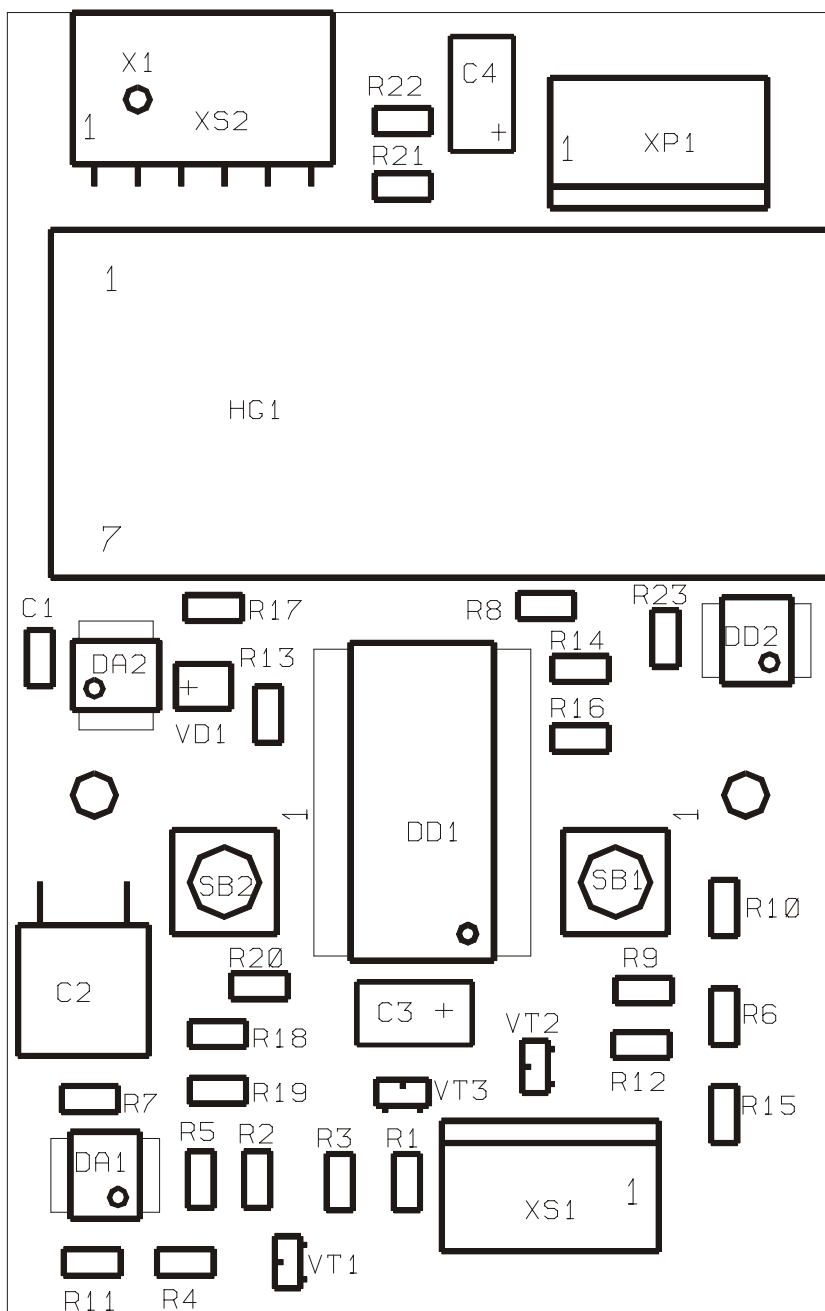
Сборочный чертеж платы обработки ФП-12. Сторона монтажа.
